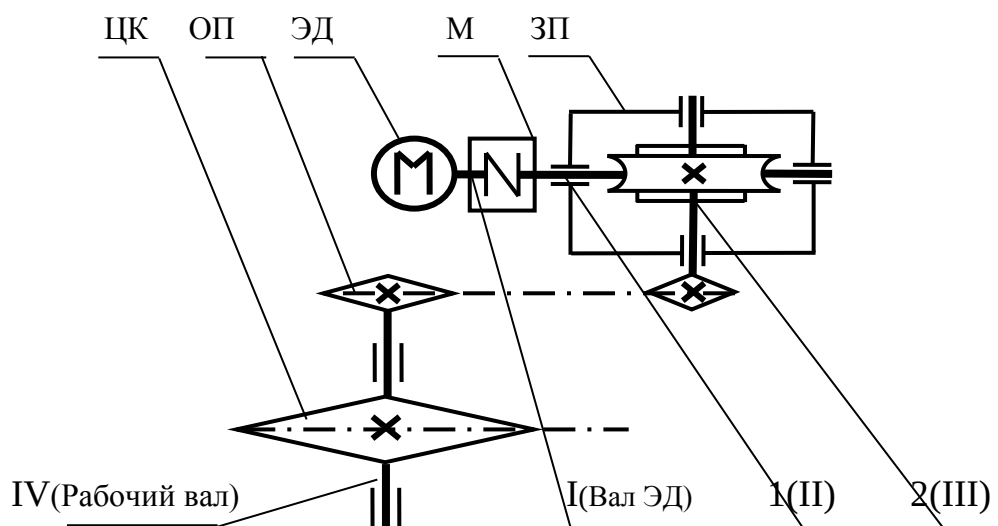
Образец схемы задания привода с червячным редуктором
